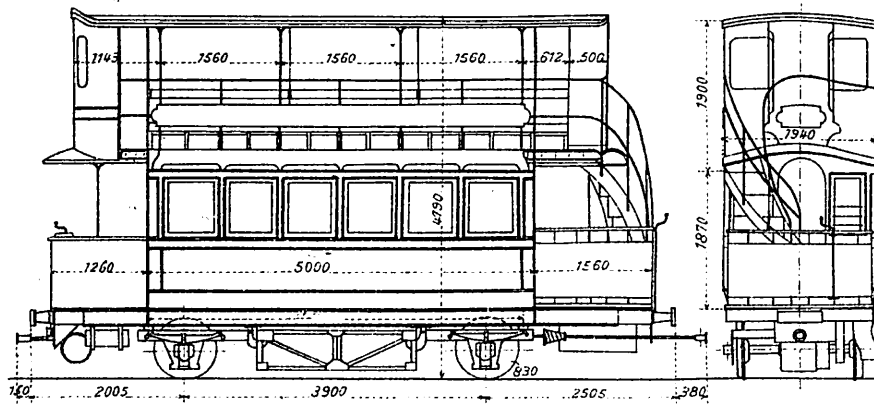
, 11. Straßenbahnwagen mit Preßluft-Antrieb.
